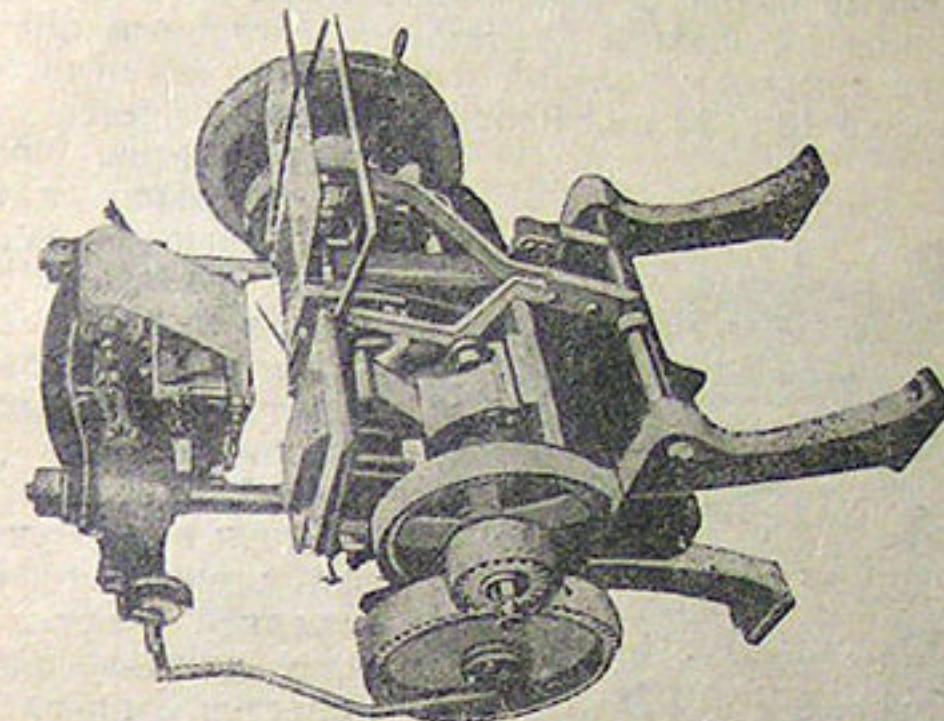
Золотопечатный механический пресс с подачей рулонной фольги.
